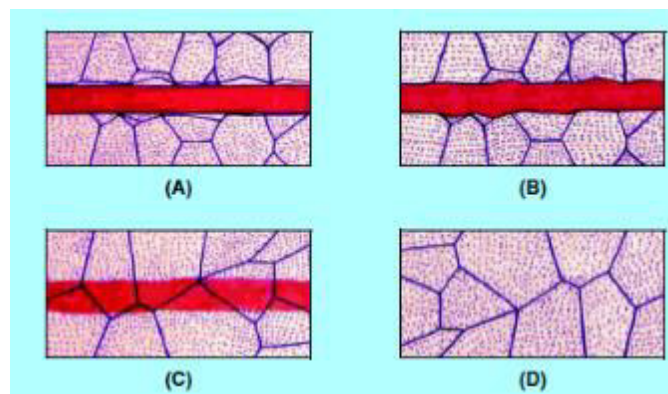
Secuencia de la soldadura fuerte por difusión.
